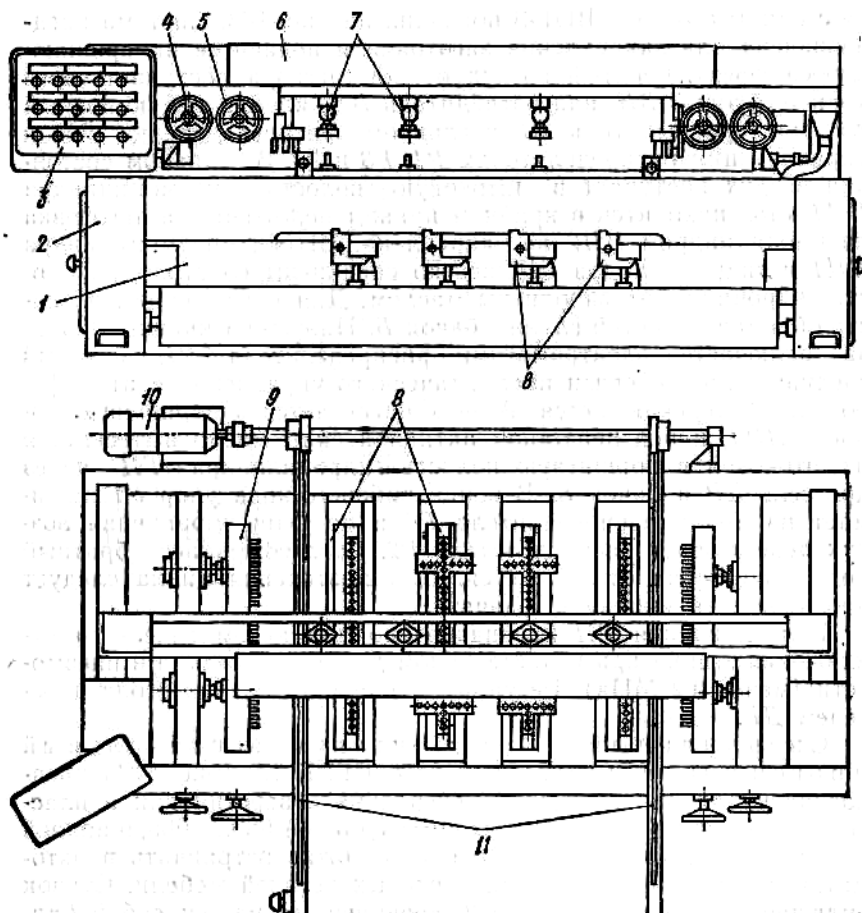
Сверлильный горизонтально-вертикальный многошпиндельный присадочный станок СГВП-1А:
